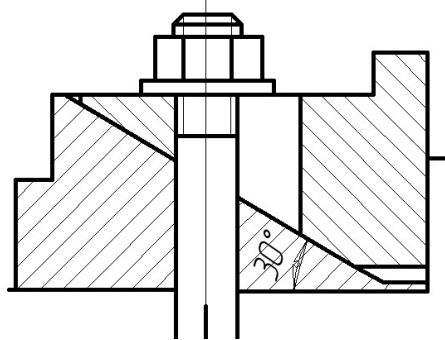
Схема клинового механізму для передавання зусилля затиску
